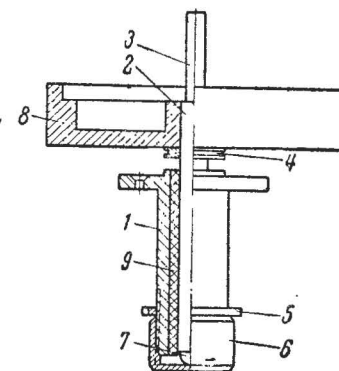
Общий вид узла ведущего вала магнитофона «Комета».
